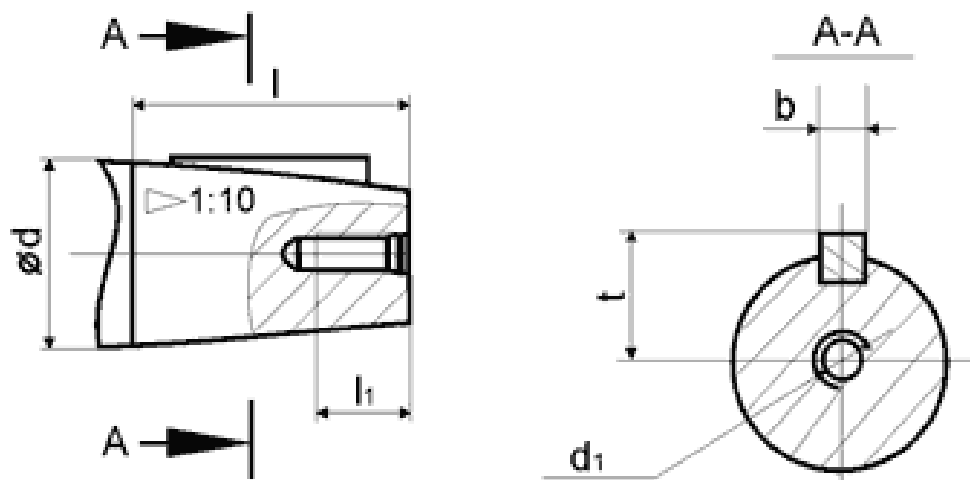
Вхідний і вихідний вали редуктора 2Ч-63
